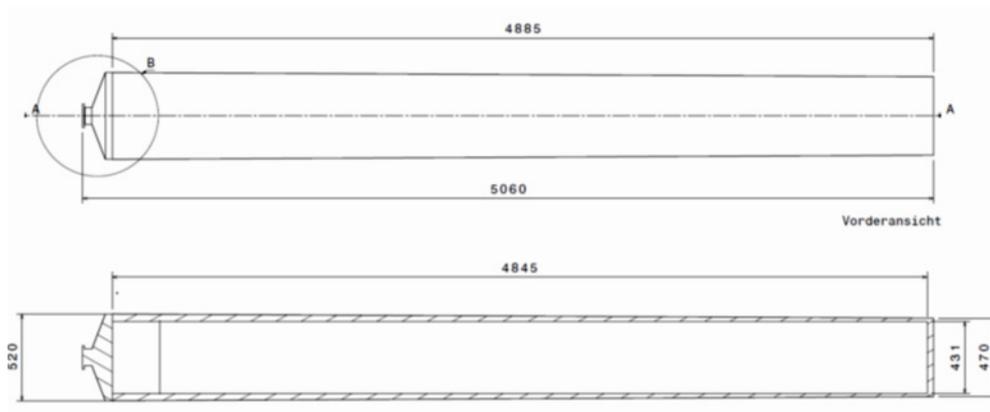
Abmessungen einer rückholbaren Brennstabkokille, aus /GRS 11/
